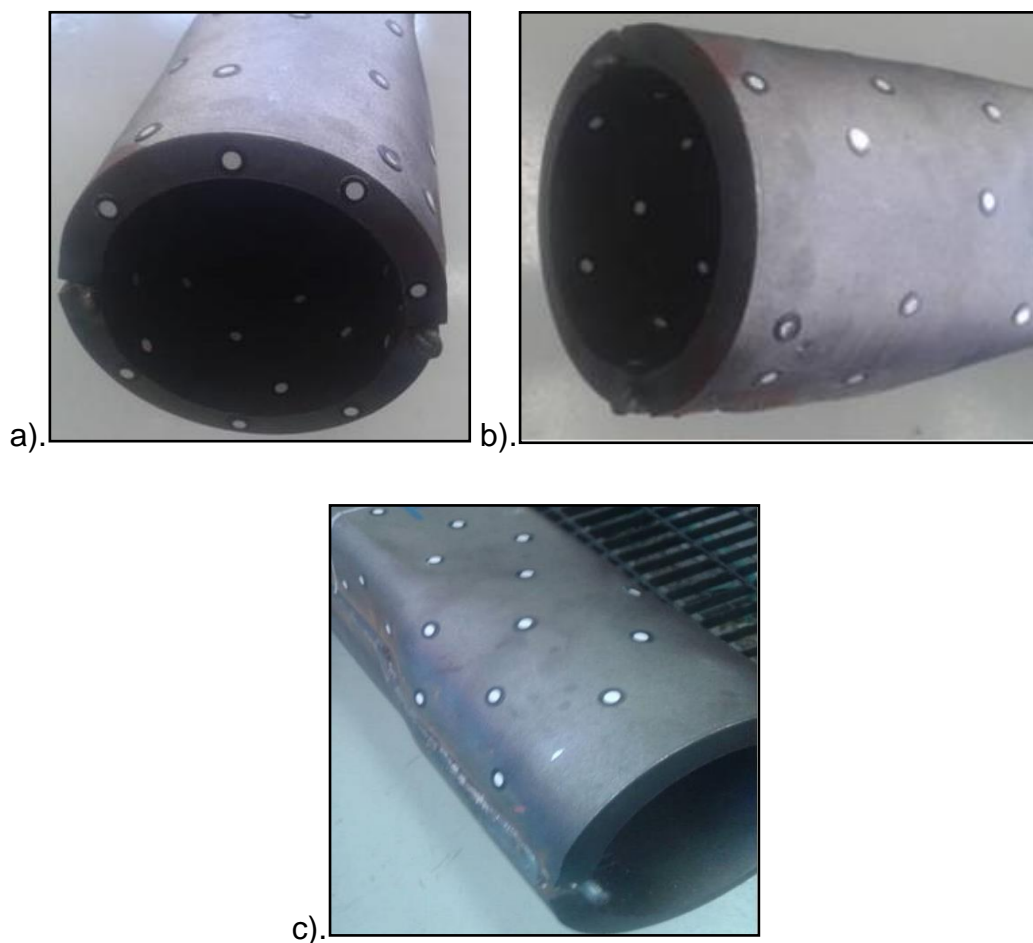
Ilustraciones de las plantillas de *targets* con elementos en diversas secciones:
